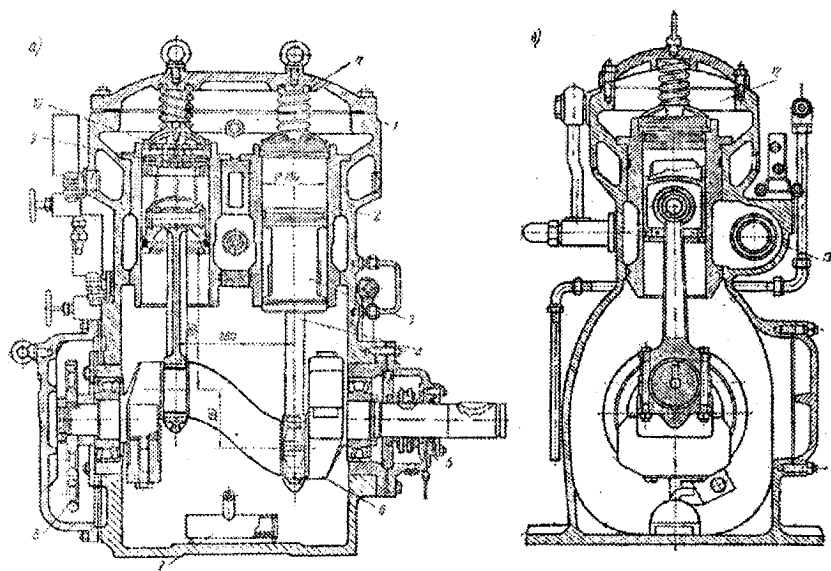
Аміачний вертикальний компресор АВ-100 (а – подовжній розріз; б – поперечний розріз): 1 – блок-картер; 2 – гільза циліндра; 3 – поршень; 4 – шатун; 5 – сальник; 6 – колінчастий вал; 7 – масляний фільтр; 8 – шестерний масляний насос; 9 – всмоктуючий клапан; 10 – нагнітальний клапан; 11 – буферна пружина; 12 – нагнітальна порожнина; 13 – всмоктуючий колектор.
